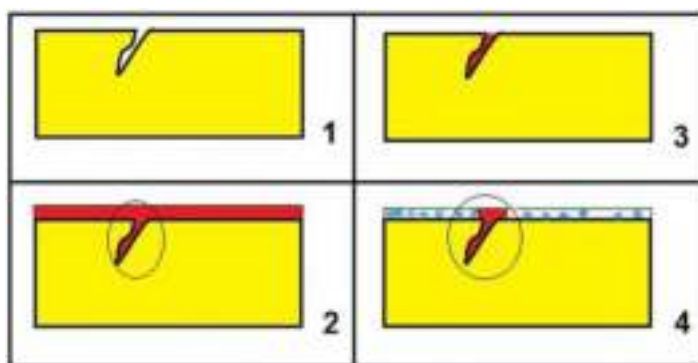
Контроль сварных соединений пенетрантом
